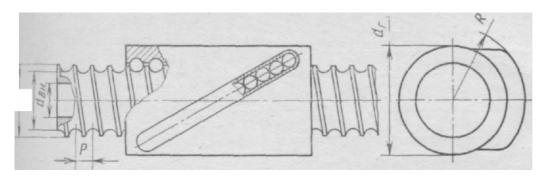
Конструктивная схема винтовой пары качения подающего механизма.
